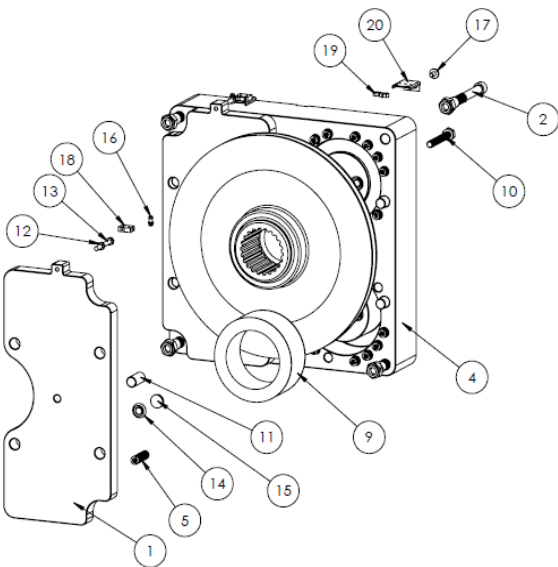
Vista en despiece del conjunto de bobinas de frenos AEMF5-11
